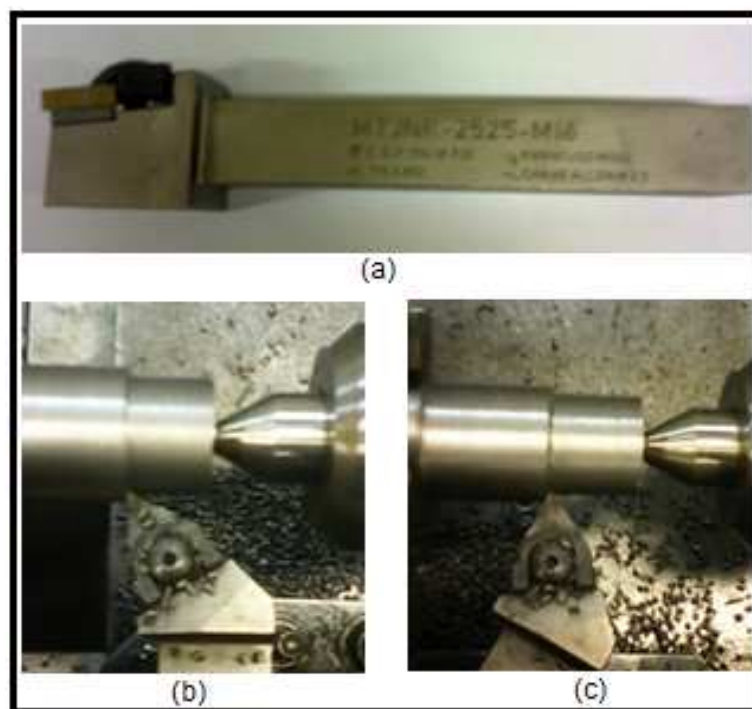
Porta ferramenta com inserto (a). Ferramenta de corte em operação de usinagem utilizando ângulo de posição de 90° (b) e 60° (c).
